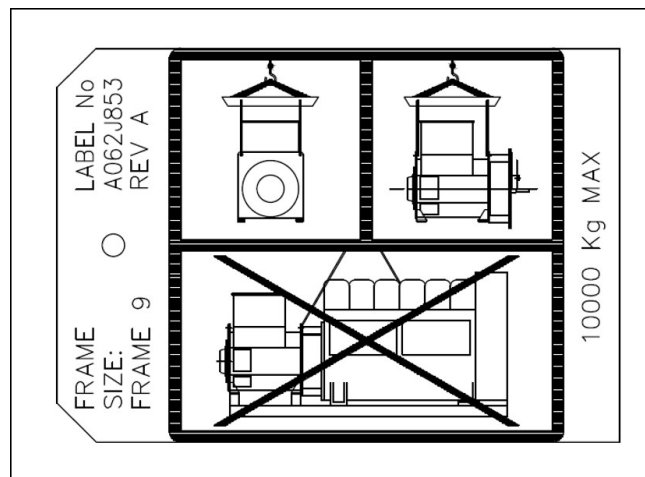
ETIQUETA DE ELEVAÇÃO
